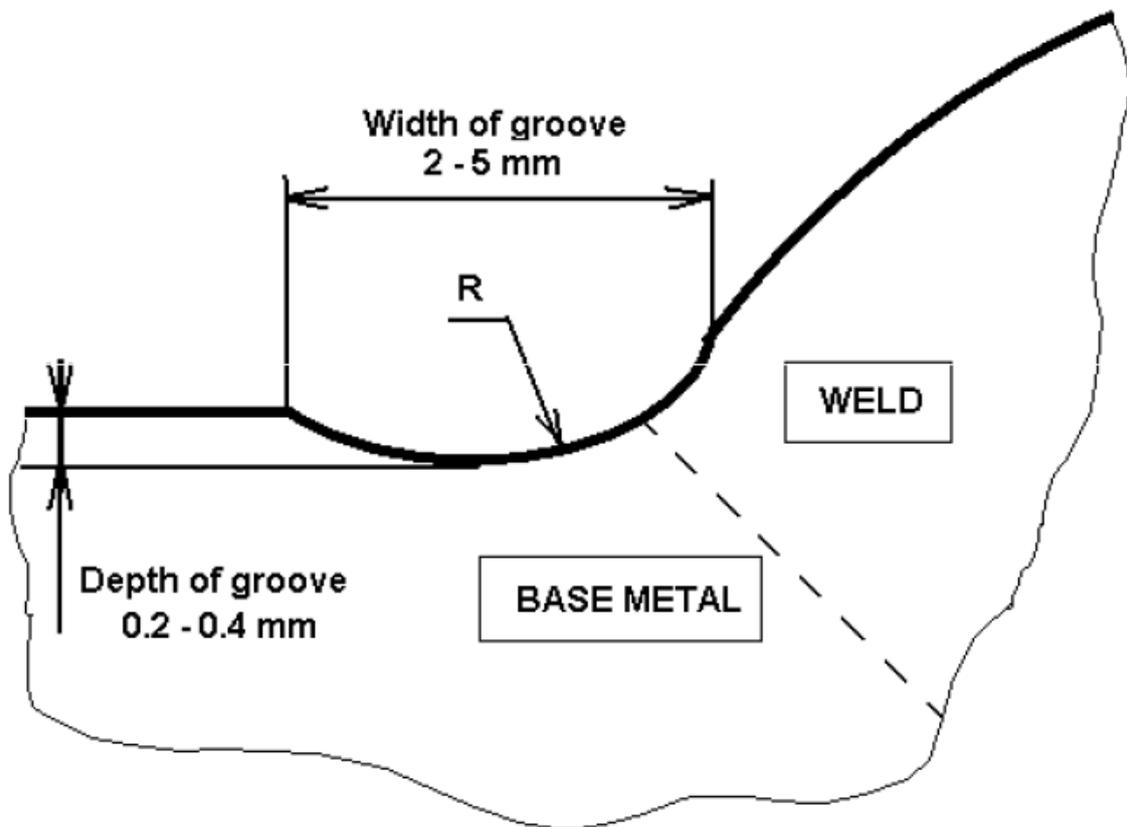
Efecto del needle peening sobre el cordón de soldadura
